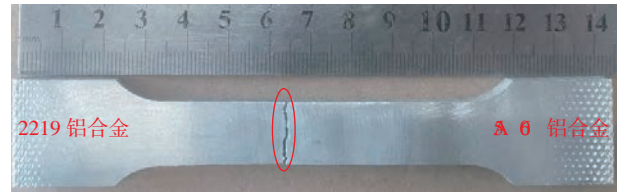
脉冲 VP-TIG 焊接头断裂位置
